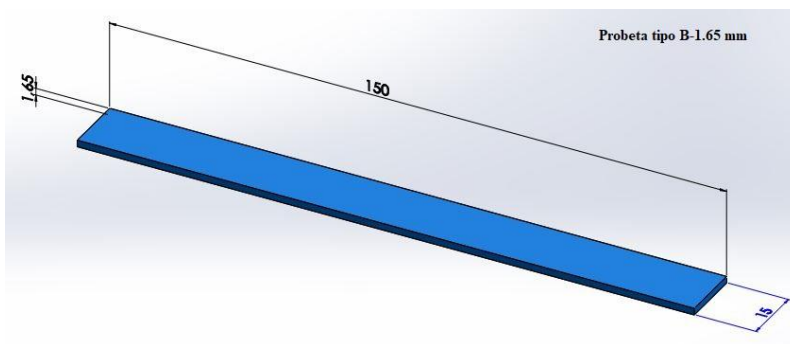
Dimensiones probeta tipo B 1,65 mm de espesor
